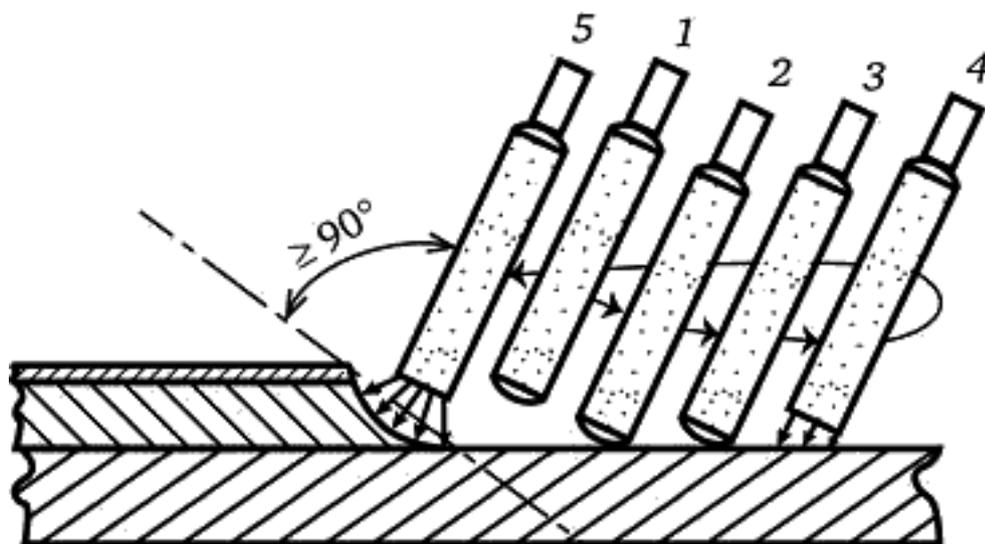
Зажигание сварочной дуги для продления сварного шва
